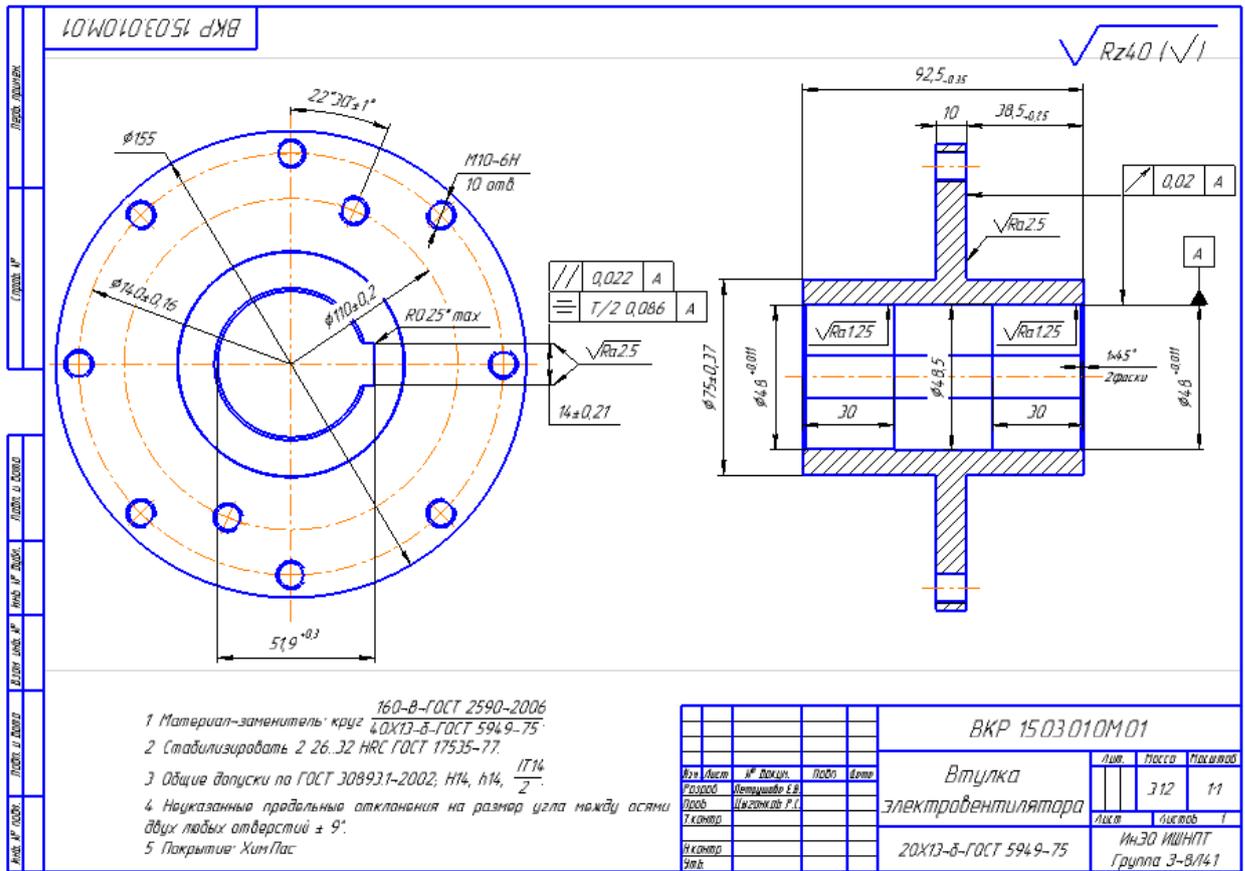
Чертеж детали «Втулка электроventилятора»
